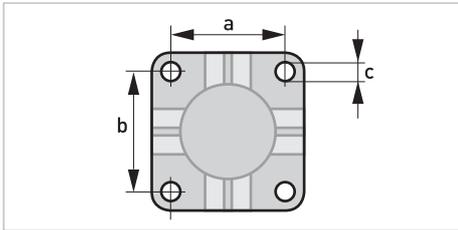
Dimensions pour plaque de montage du boîtier intempéries
